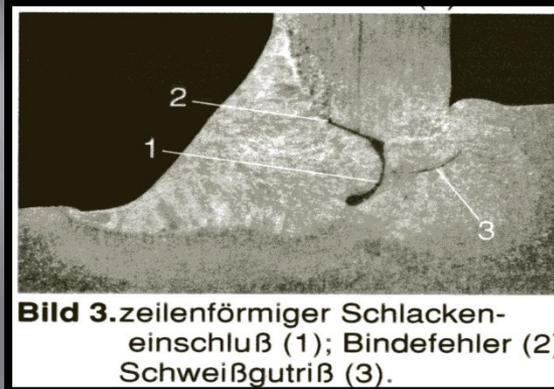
zeilenförmiger Schlackeneinschluss (1); Bindefehler (2); Schweißgutriß (3).
